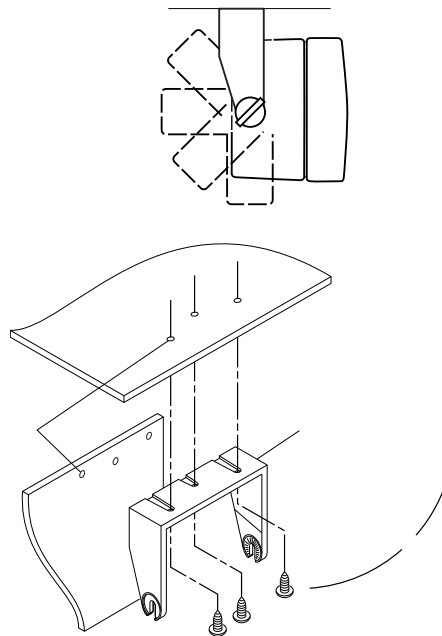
Montage des Lautsprechers unter dem Armaturenbrett
